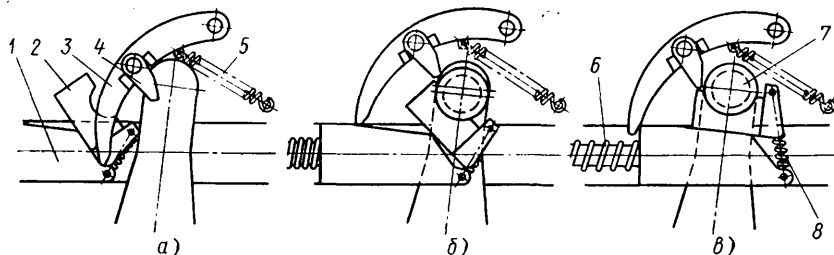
Схема работы однозахватного разъемно-сцепного механизма фирмы ТЕНА: а — механизм подготовлен для сцепки; б — сцепной шкворень в механизме; в — сцепка завершена
